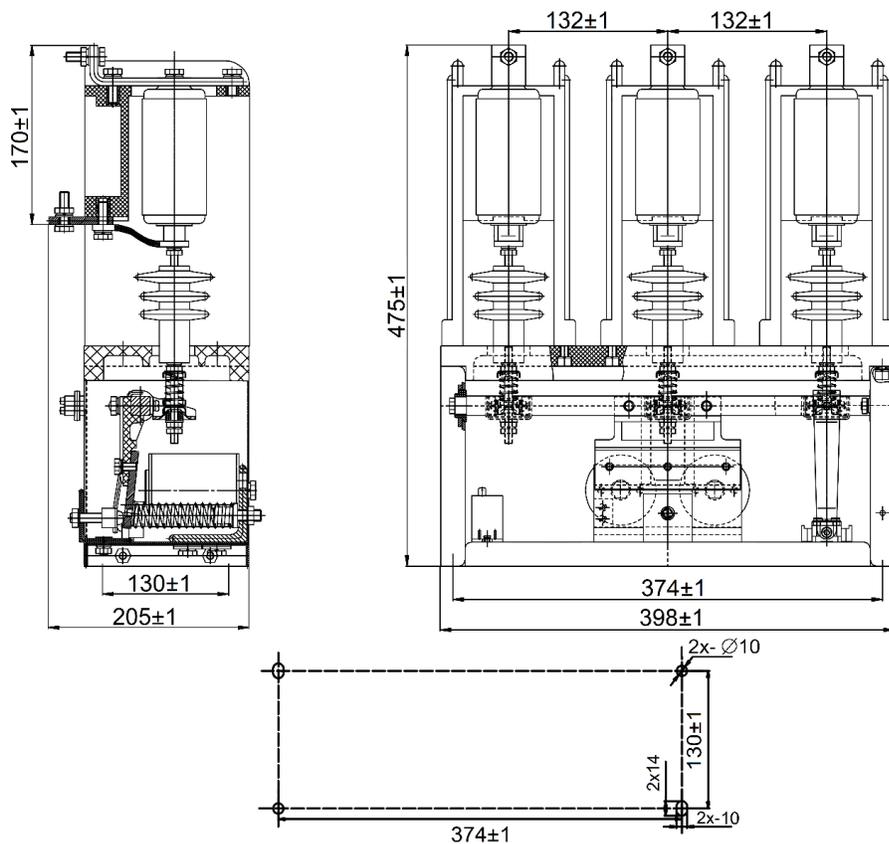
Габаритные размеры контакторов КВТ-6 на номинальные токи 160, 250, 400, 630 А трех полюсного исполнения и размеры монтажной площадки.
